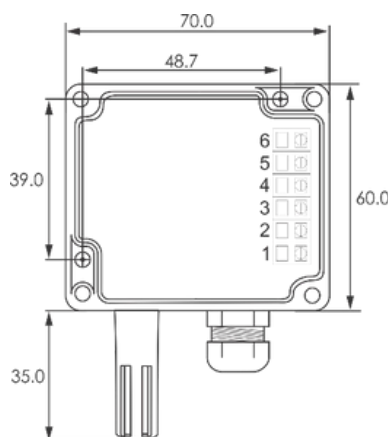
Fori di montaggio e dimensioni per il modello RHT-WM (in millimetri)
